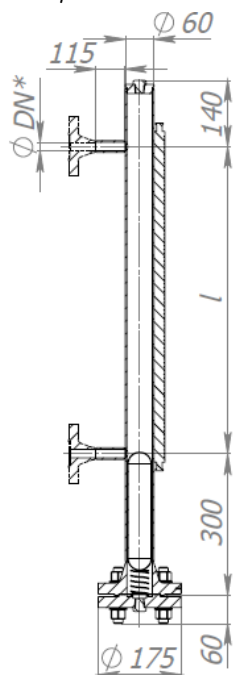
Габаритные и присоединительные размеры указателя уровня дапасного SIRIUS 6,3 МПа
